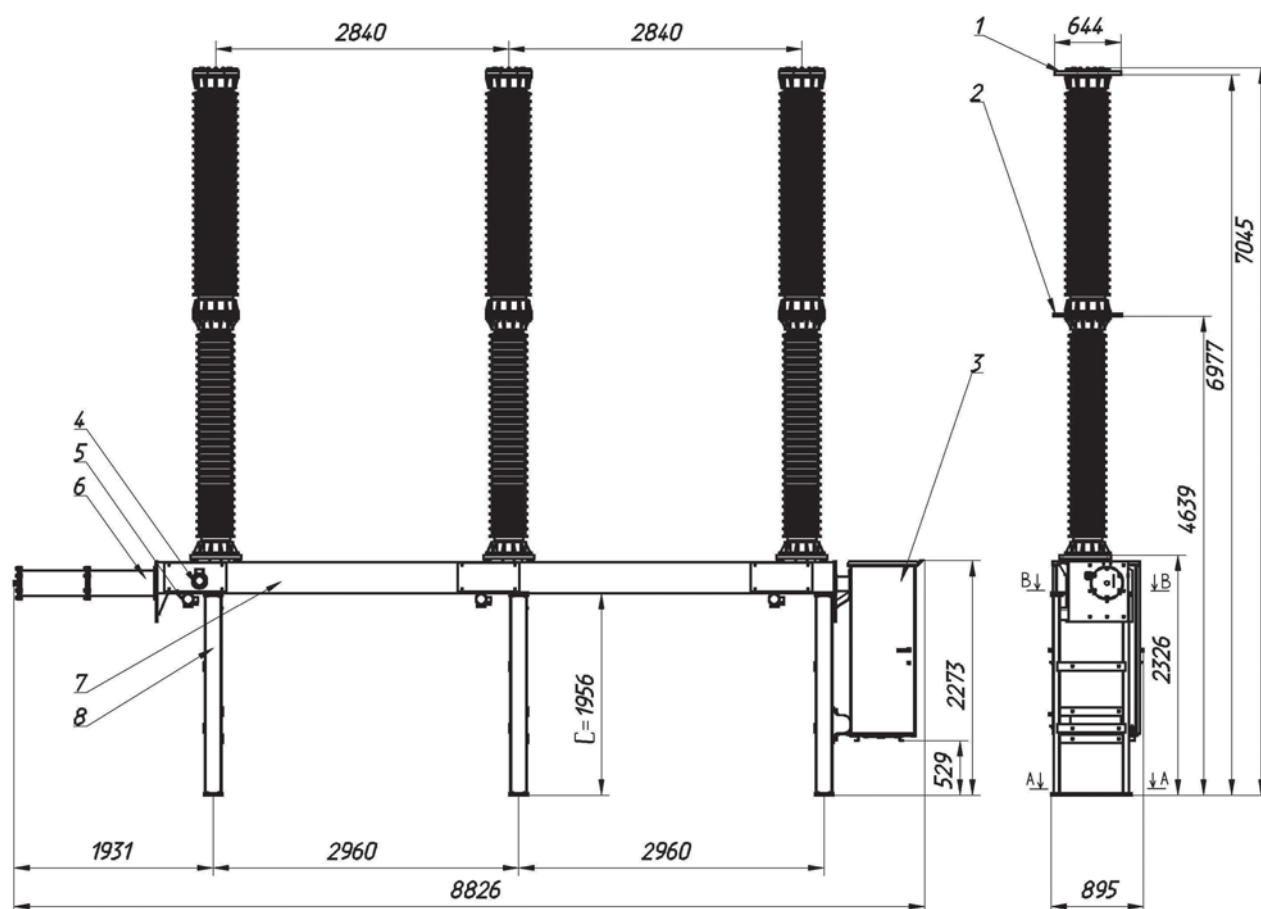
Габаритные размеры выключателя элегазового колонкового ВГТ-1А1-220.
